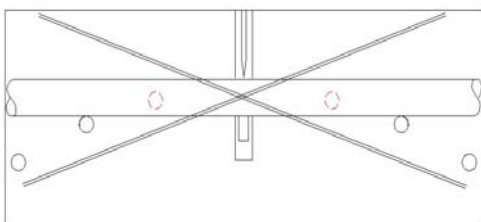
Гибочный стержень установлен для диаметра шланга DN20 3/4"
